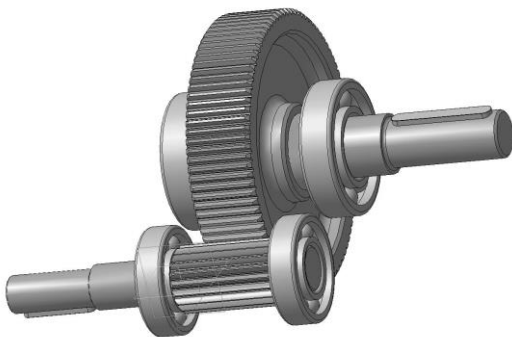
Загальний вид прямозубчастої циліндричної передачі
